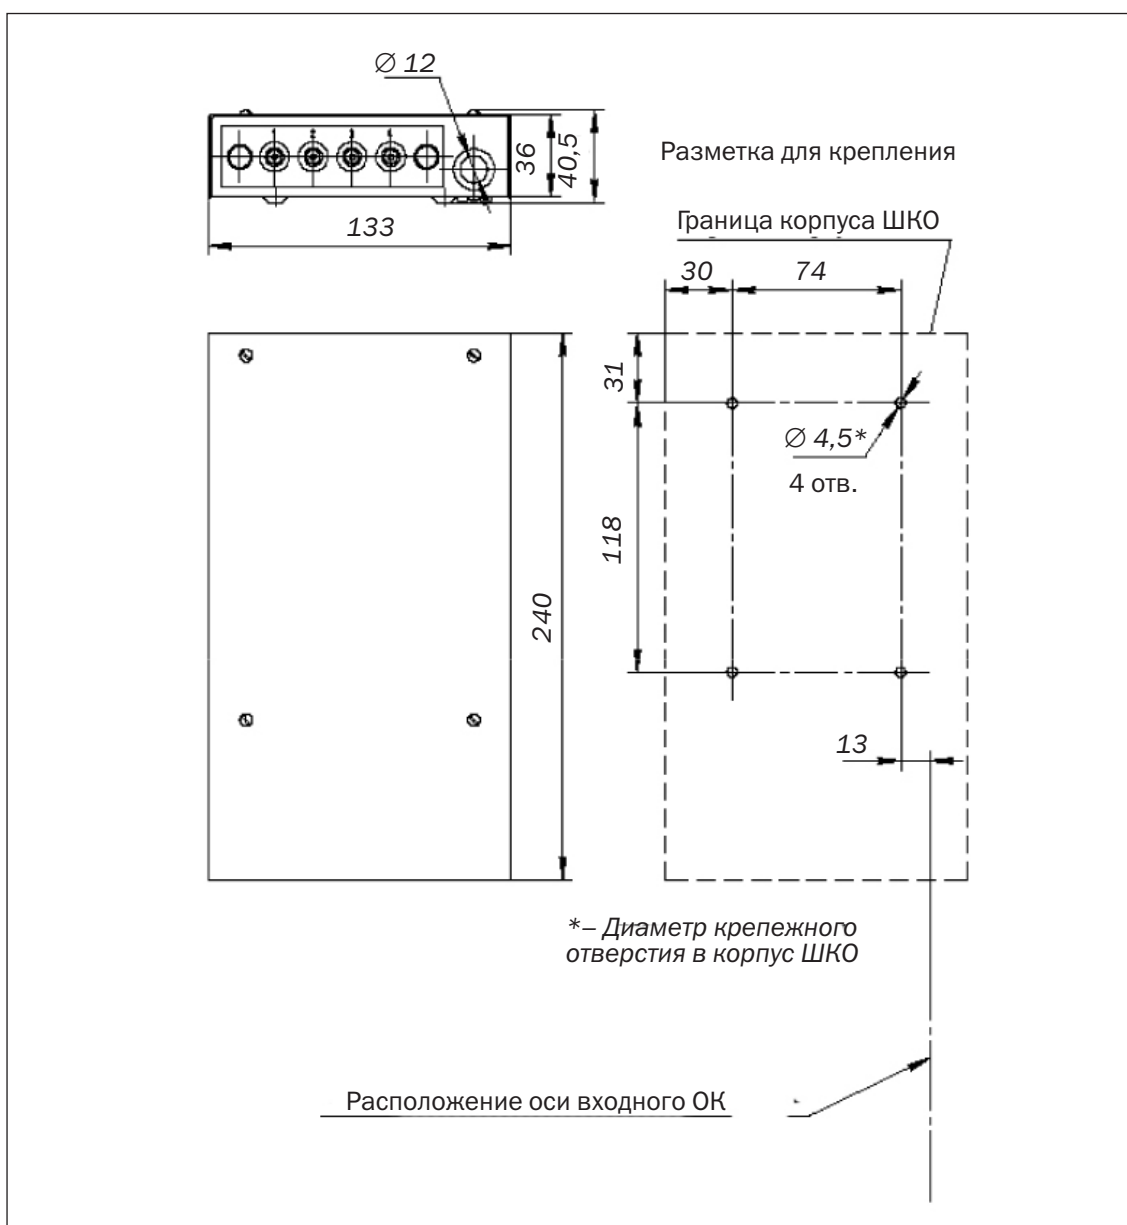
Габаритные и установочные размеры шкафа
